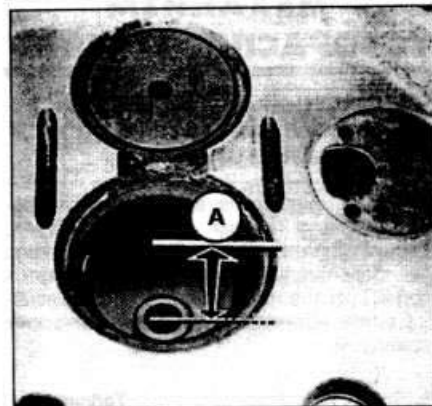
Размер «А» между торцом направляющей втулки клапана и плоскостью головки цилиндра
